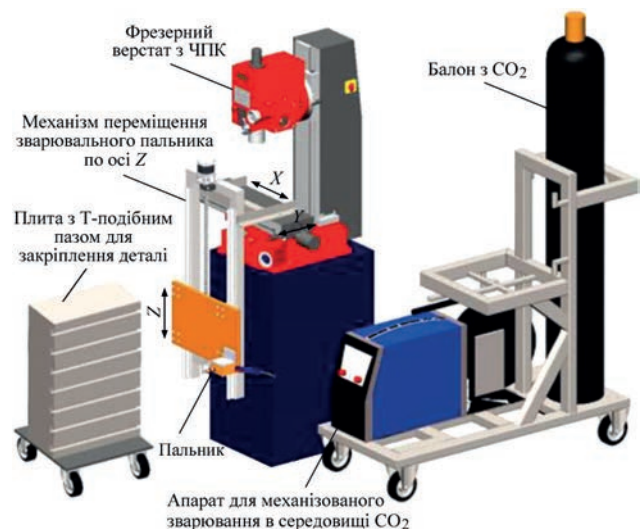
Схема установки для адитивного наплавлення способом MAG із трикоординатною системою переміщення на базі фрезерного верстату
